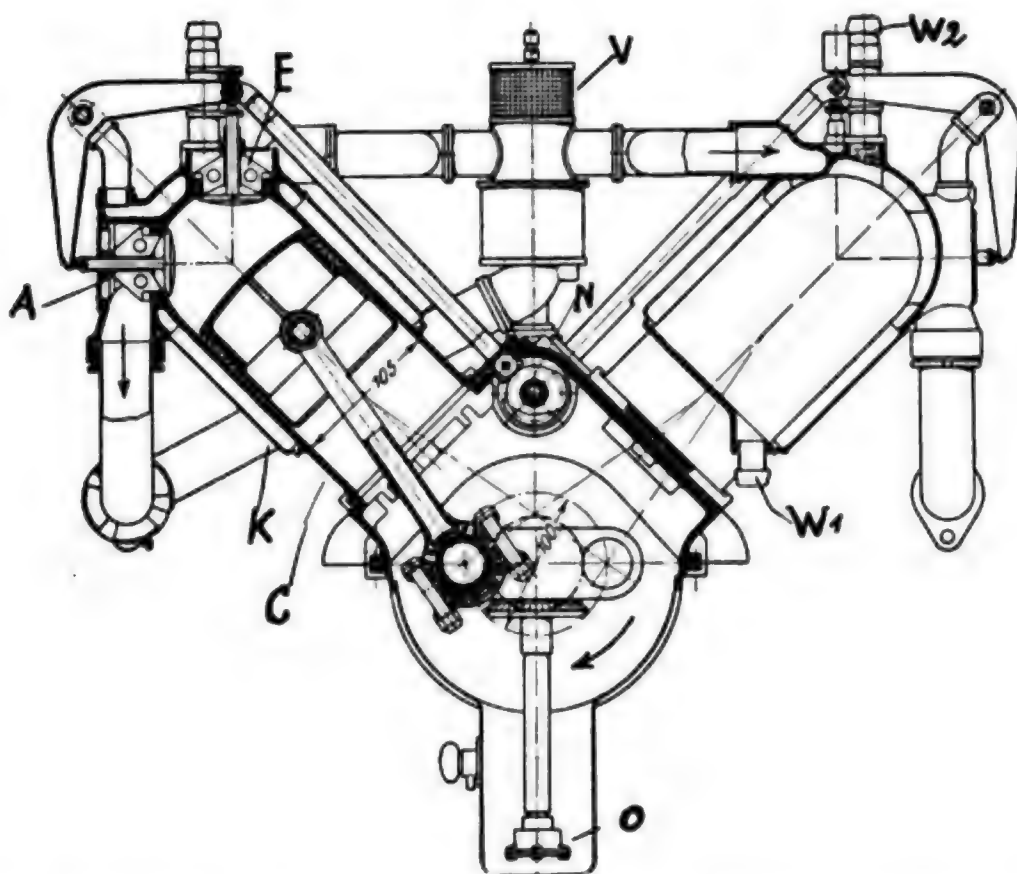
Schnitt durch den Flugmotor von Rumpler. A Auslaß, E Einlaßventil, C Zylinder, K Kühlmantel, W₁ Wassereinlaß, W₂ Wasserauslaß, N Steuerwelle, V Vergaser, O Ölpumpe.
